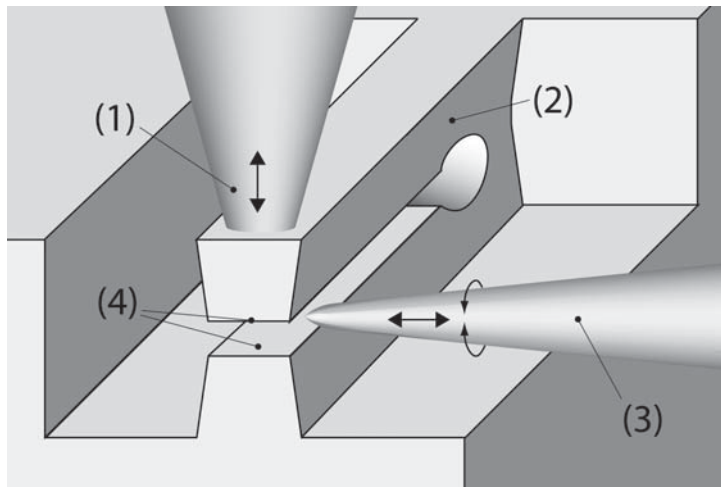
Aufbau im Submikro- und Nanobereich schematisch: Das rückfedernden Umformwerkzeug (2) wird durch das abgeflachte Werkzeug (1) betätigt und formt das Halbzeug (3) zwischen den Umformflächen (4) um.
